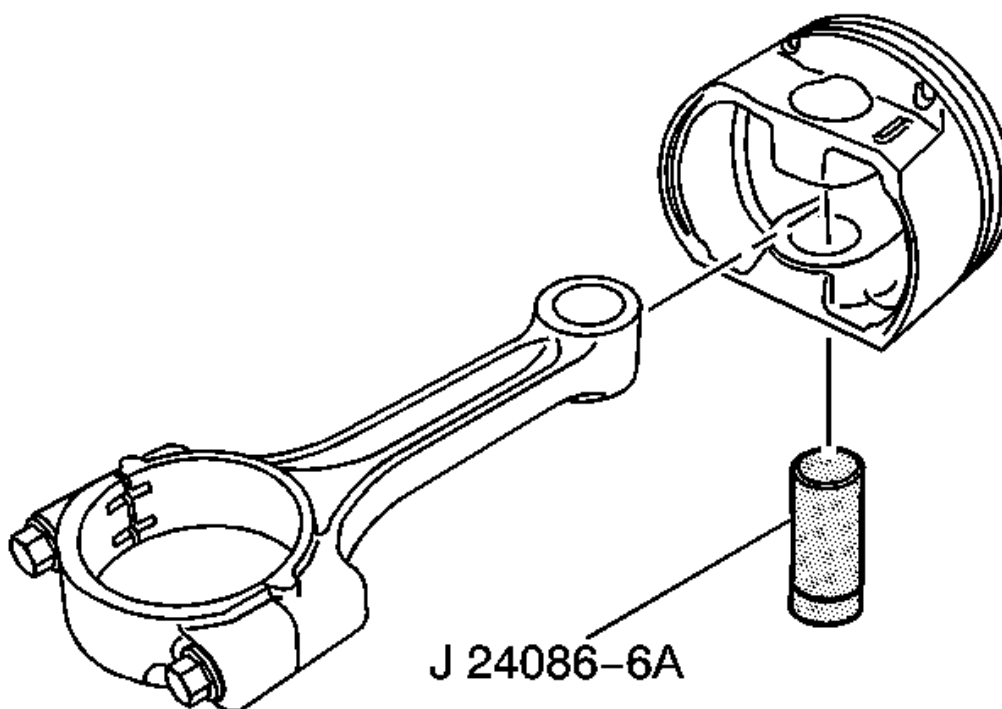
Ensamble J 24086-C Con conjunto de pistón
